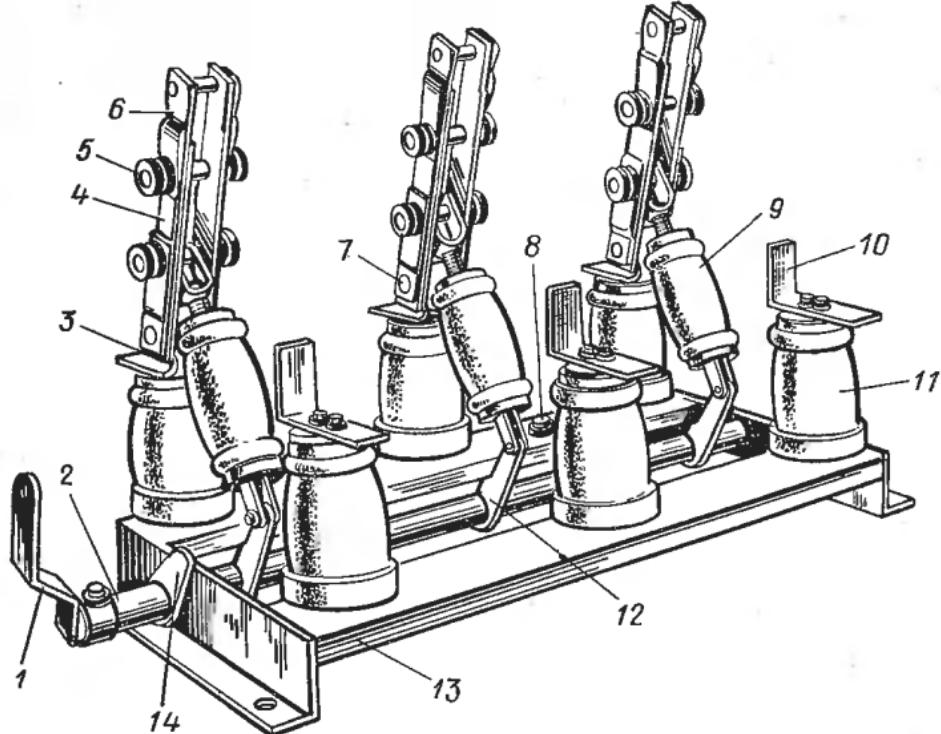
Трехполюсный разъединитель РВ-10/600:
